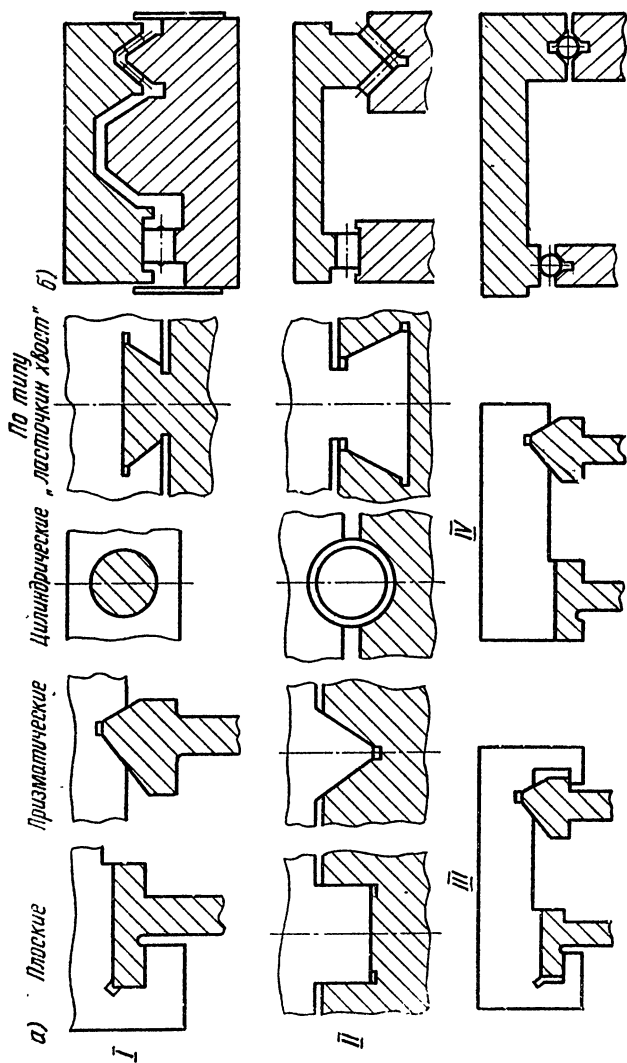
Конструкции направляющих: а — скользящие; б — качения
